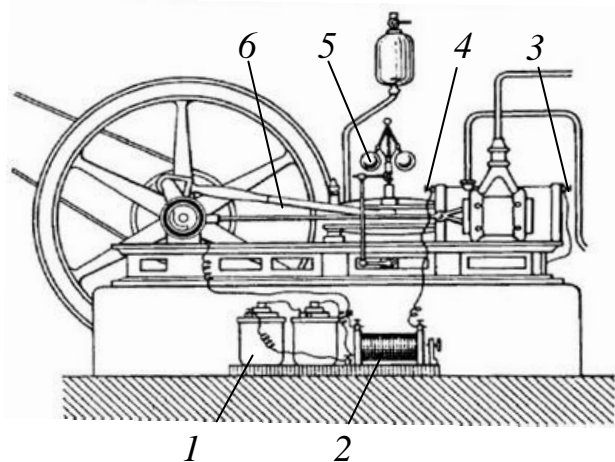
Общий вид двигателя Ленуара, 1859 г.:
